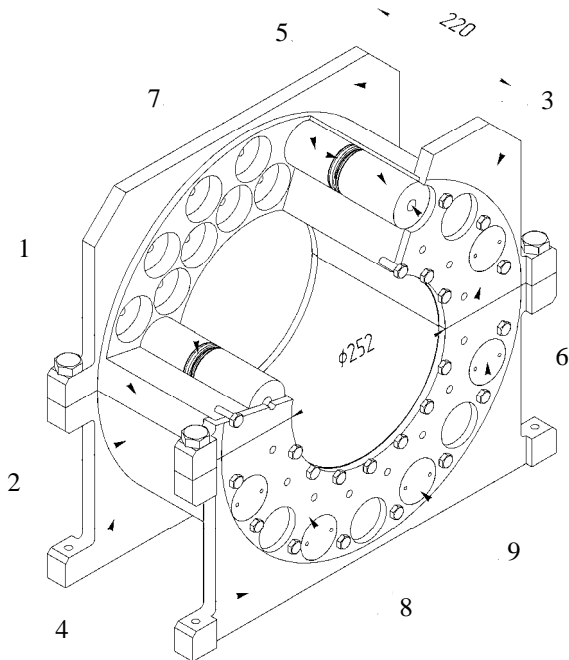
Реакторный умножитель нейтронов РУН-1: 1 – верхняя половина цилиндра (матрица); 2 – нижняя половина цилиндра (матрица); 3 – верхняя крышка; 4 – нижняя крышка; 5 – стержни из ^{235}U , 14 пар – наружный ряд, 16 пар – внутренний ряд; 6 – толкатели; 7 – тарельчатые пружины; 8 – листовой кадмий; 9 – пробки
